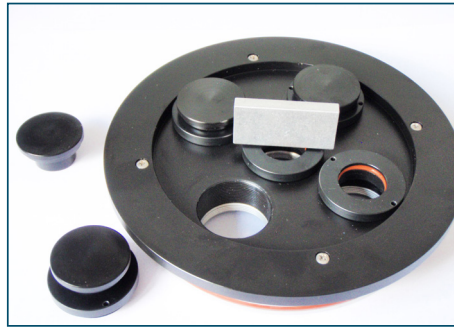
Anschlussadapter und Demontagewerkzeug
